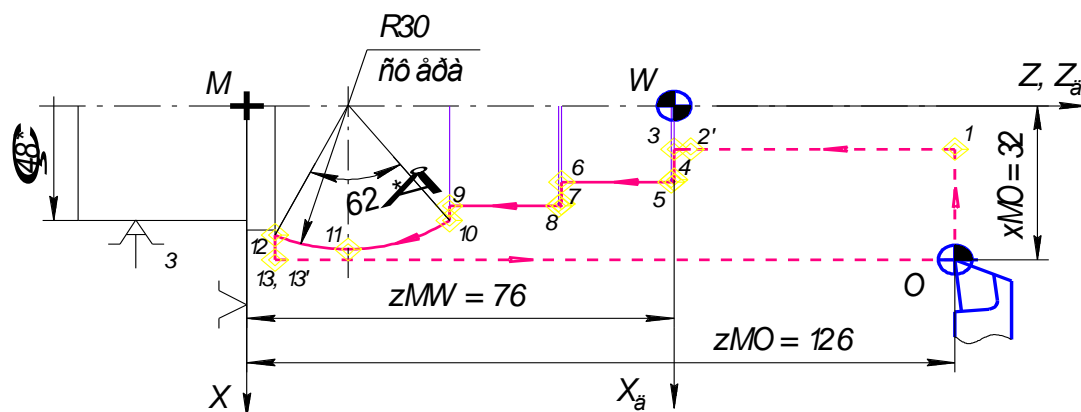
Операційний ескіз деталі "Опора" (перший установ, чистове точіння)
